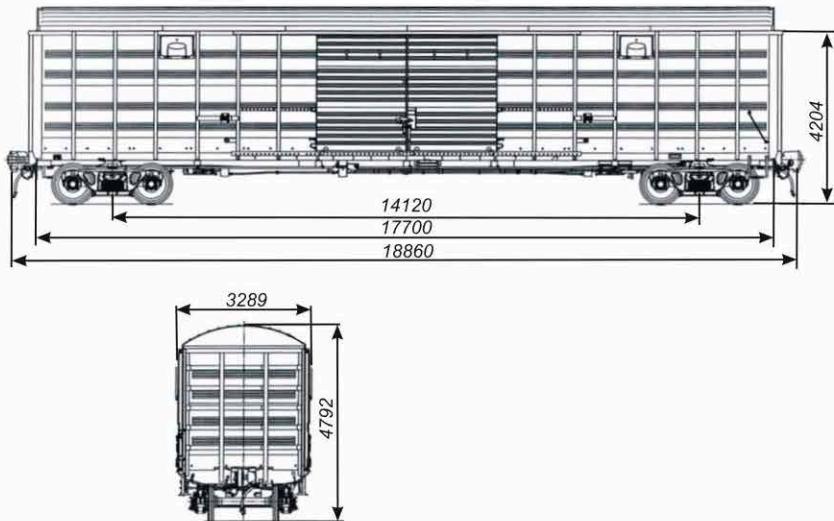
Схема общего вида универсального четырехосного крытого вагона модели 11-2135-01
